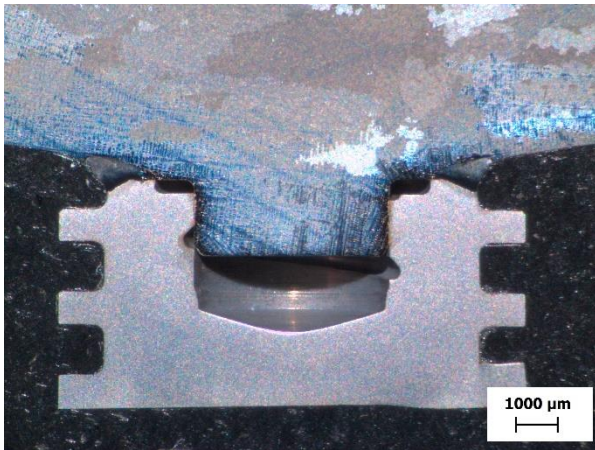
Inconel 713C+42CrMo4 leptadlo Adler
